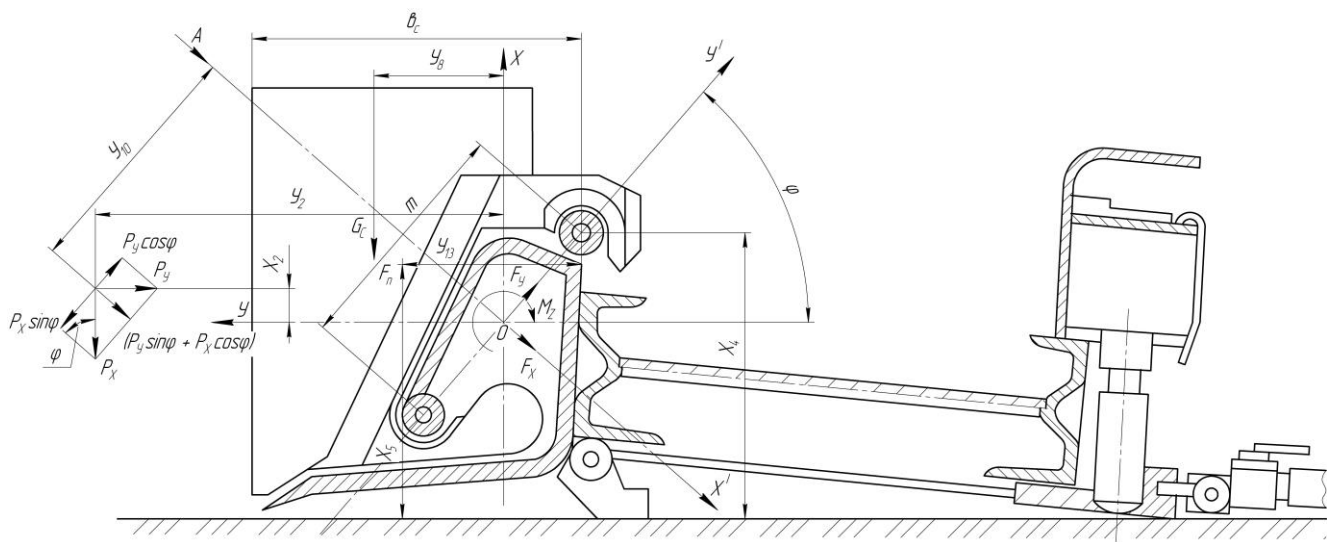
Вид сбоку исполнительного органа струговой установки скользящего типа
